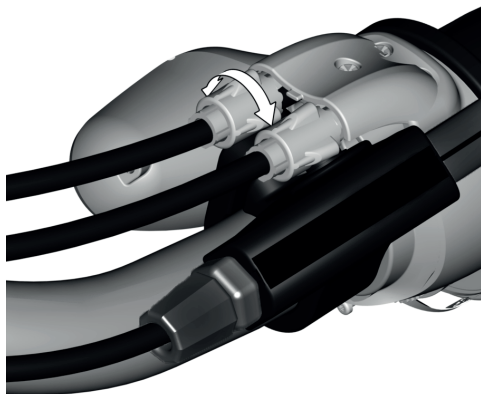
Reduzierung oder Erhöhung des Kabelspiels durch Drehen der Zugeinstellschraube am Griffschalter
